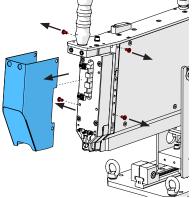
Desmontaje de la cubierta protectora del cabezal
